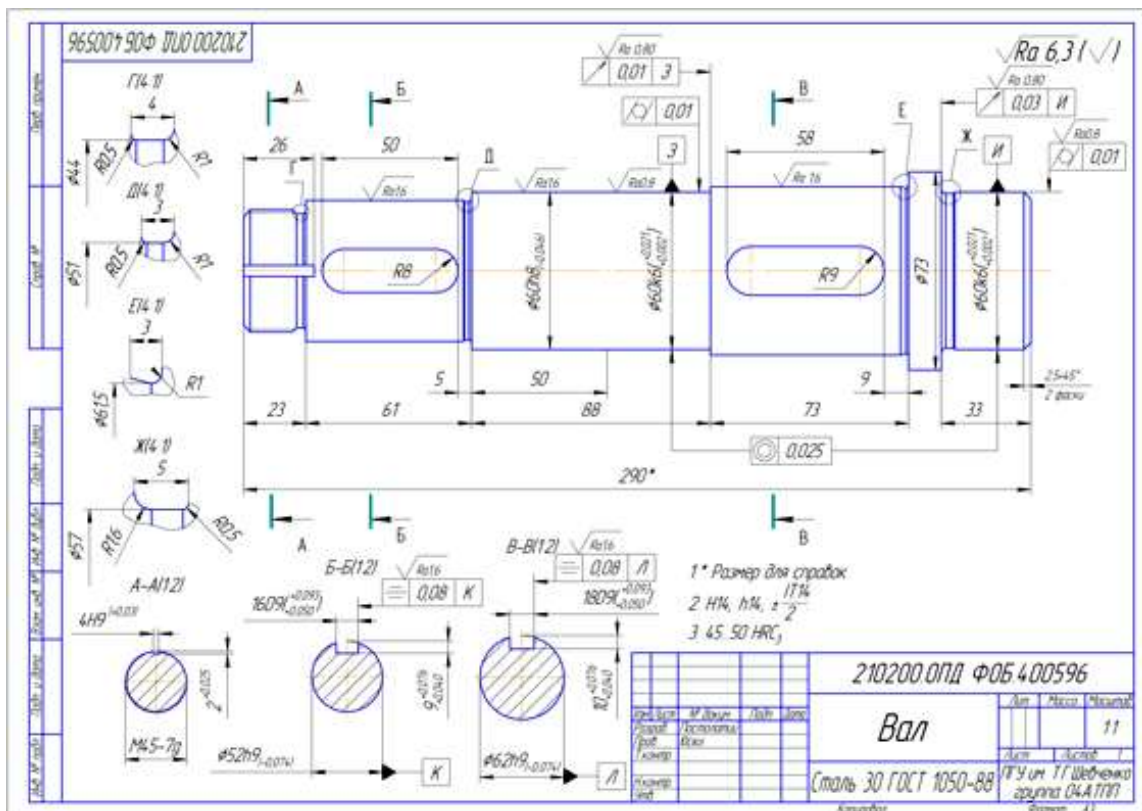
Пример выполнения рабочего чертежа Вал
